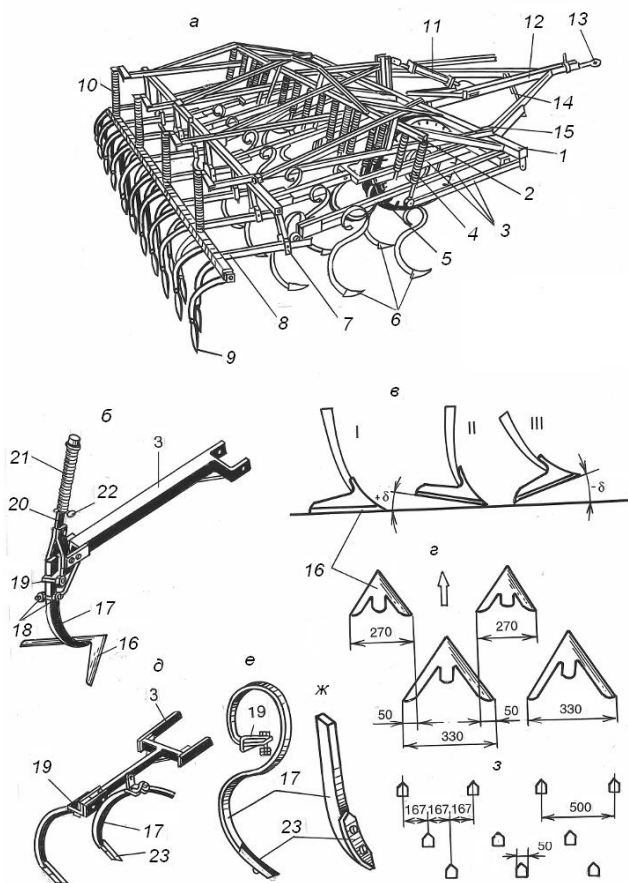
Культиватор КПС-4: а – общий вид культиватора КПС-4; б – универсальная стрельчатая лапа; в – варианты установки лапы: I – на рыхлых почвах; II – на плотных почвах; III – неправильная установка; г и з – расстановка стрельчатых и рыхлительных лап; д, е, ж – рыхлительные лапы на С-образной (дугообразной), S-образной и жесткой стойках; 1 – рама; 2 – уголок; 3 – грядили; 4 – штанга с пружиной; 5 – колесо; 6 – рабочие органы; 7 – понизитель; 8 – приспособление; 9 – пружинная боронка; 10 – штанга с пружиной; 11 – гидроцилиндр; 12 – сница; 13 – прицепная серьга; 14 – подставка; 15 – регулятор глубины; 16 – стрельчатая лапа; 17 – стойка; 18 – болты; 19 – держатель; 20 – штанга; 21 – пружина; 22 – шплинт; 23 – наральник
